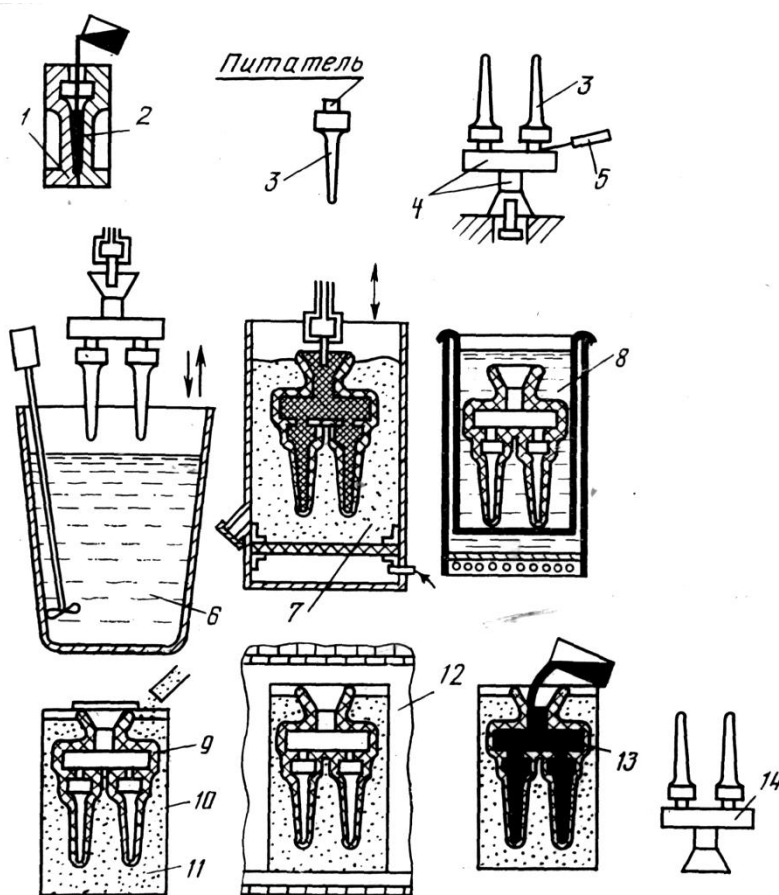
Схема изготовления отливок по выплавляемым моделям:
